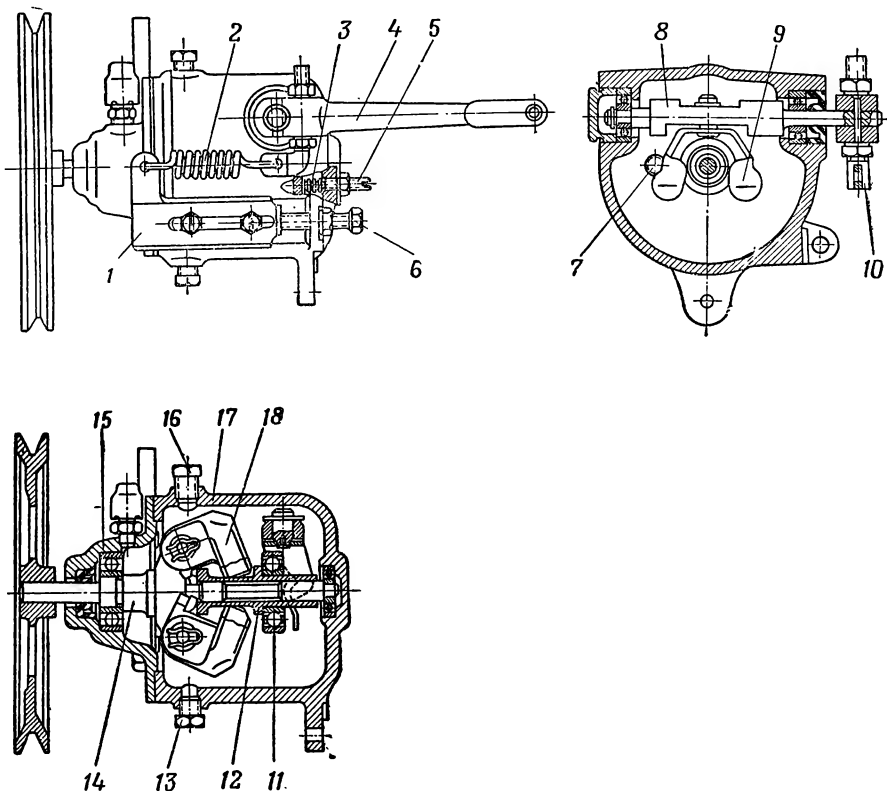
Регулятор скорости вращения коленчатого вала двигателя:
